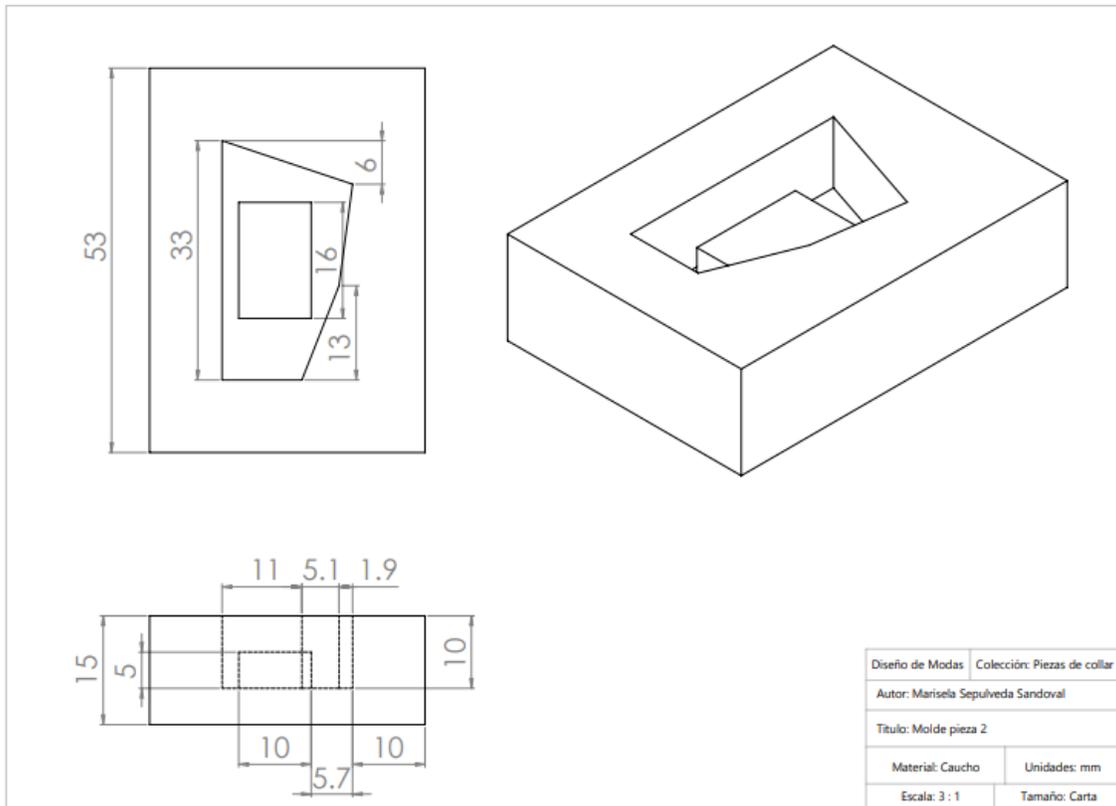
Dimensiones del contra-molde de caucho de la pieza 2.
